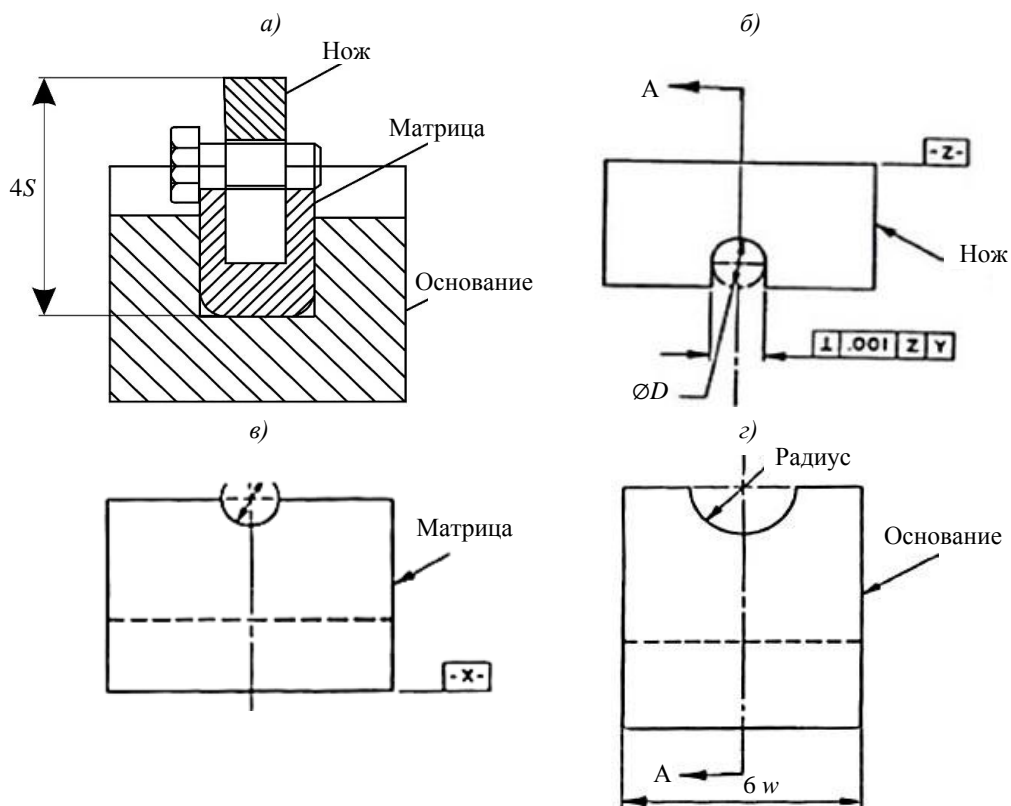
Схема приспособления с открытой матрицей: общий вид (a) и вид сбоку ножа ($б$), матрицы ($в$) и обоймы матрицы (z) [1]
